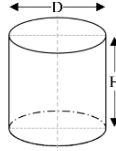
Dimensions des éprouvettes de compression et de fluage ($H=15,0\pm 0,1$ mm, $D=10,0\pm 0,1$ mm).
